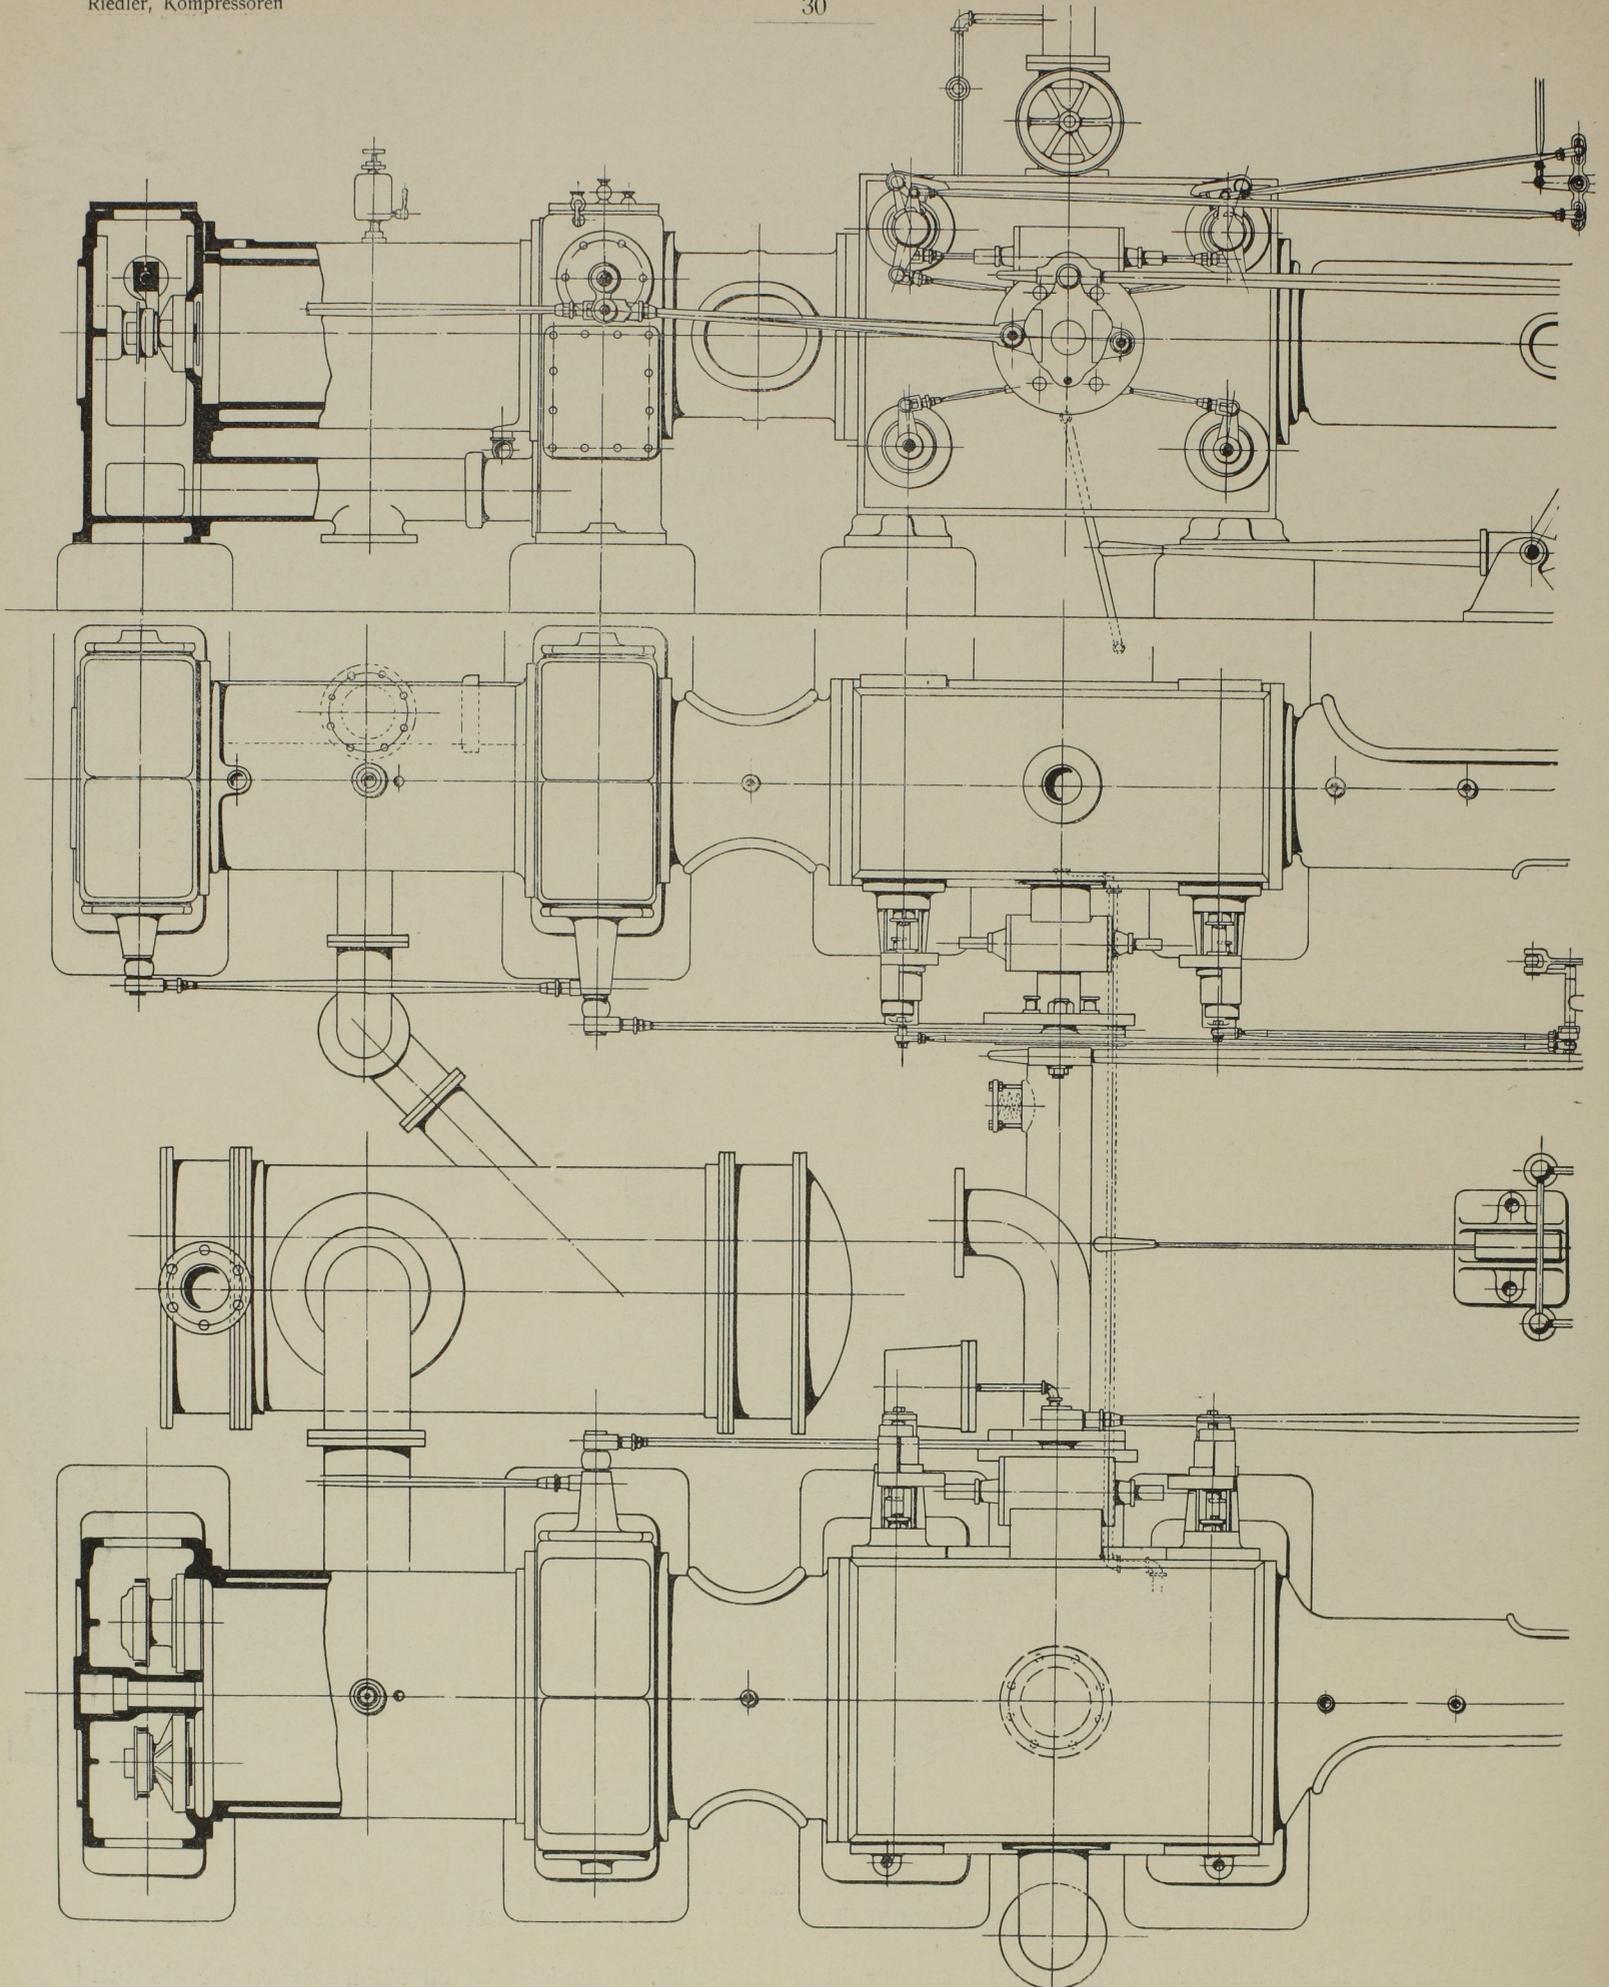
Grundriss und Seitenansicht. Massst. 1:24.
